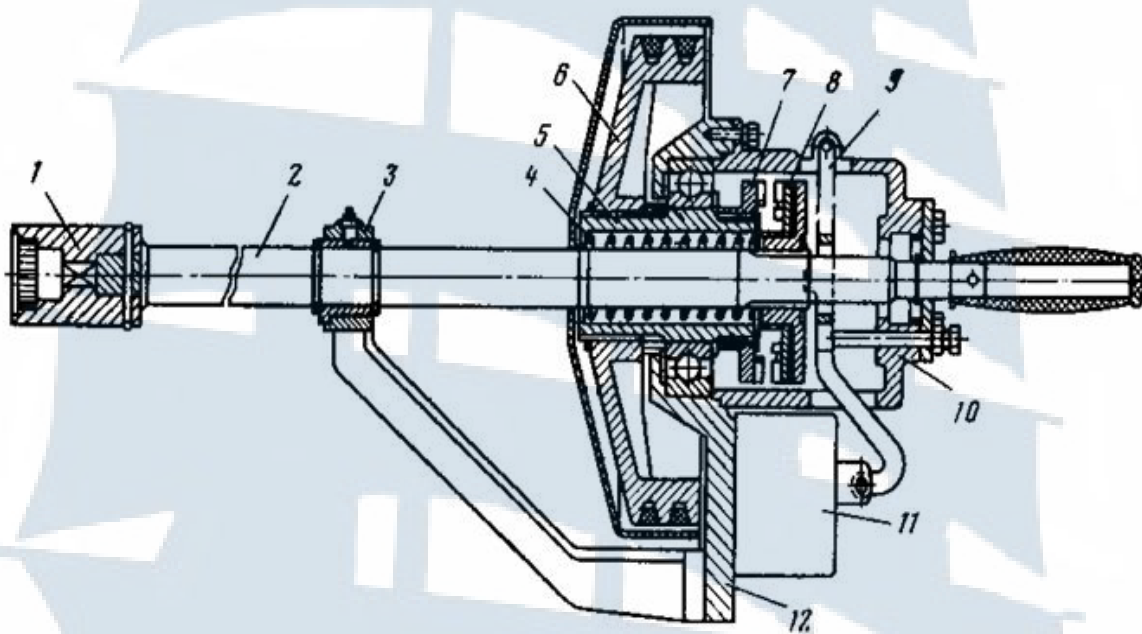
Схема ударного механизма гайковёрта для гаек колёс:
